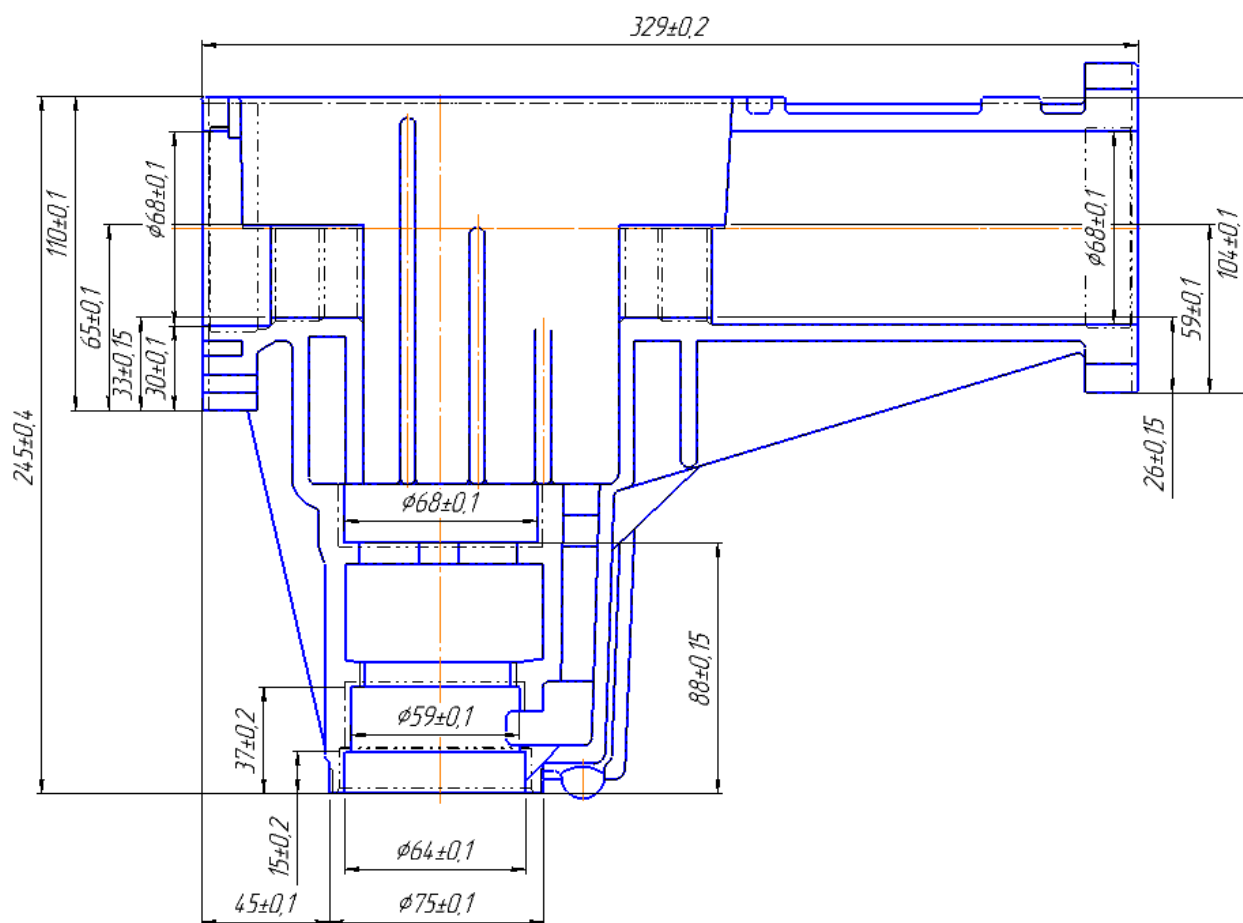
Заготовка полученная методом литья в металлическую форму под давлением
